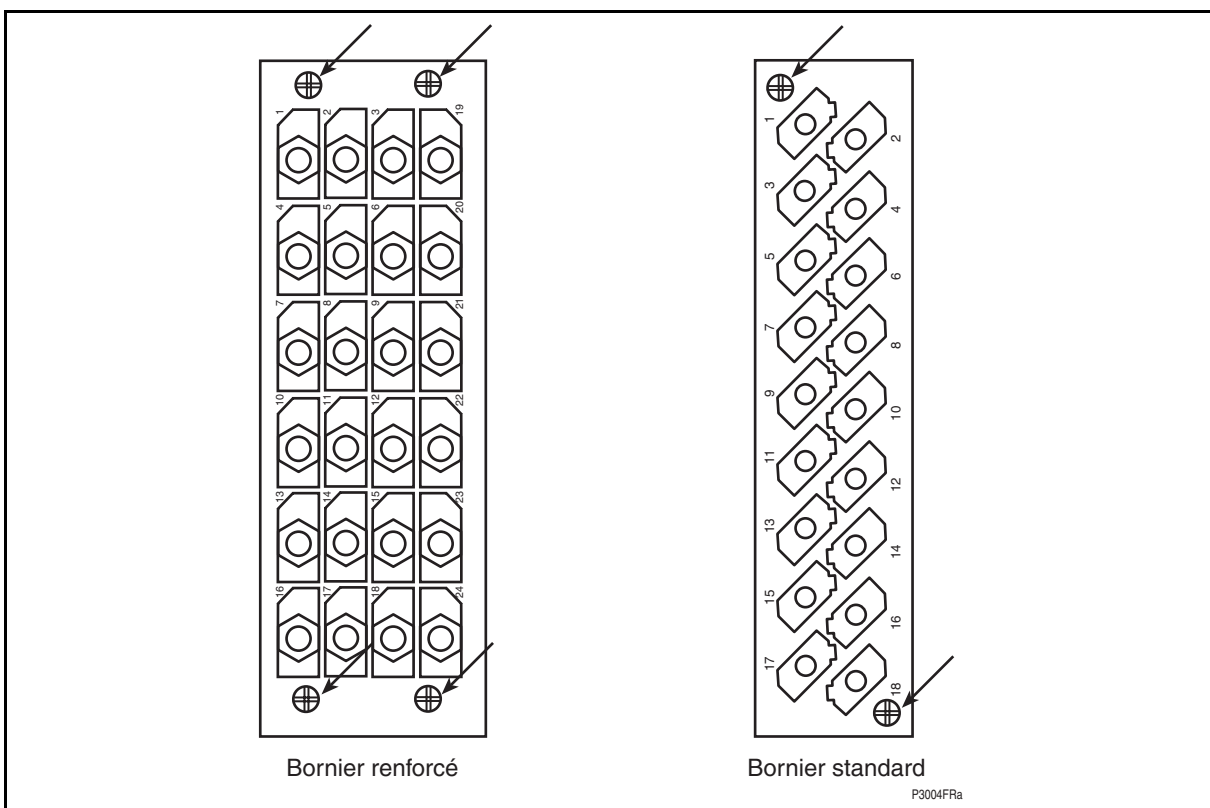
EMBLACEMENT DES VIS DE FIXATION DES BORNIER
